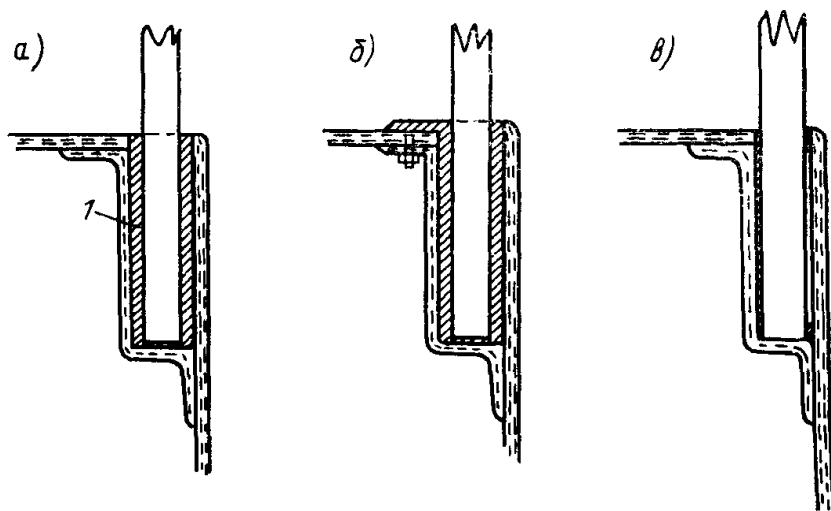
Установка стоек леерного ограждения в гнезда, расположенные под палубой: *а* — гнездо из металлической или туфоловой трубы 1, приформованное к бортовой обшивке корпуса; *б* — усовершенствованный вариант предыдущего способа. Гнездо имеет фланец, крепление болтами и заделка которого повышают водонепроницаемость соединения; *в* — гнездо отформовывается непосредственно вокруг концевой части стойки, пропущенной сквозь палубу.
